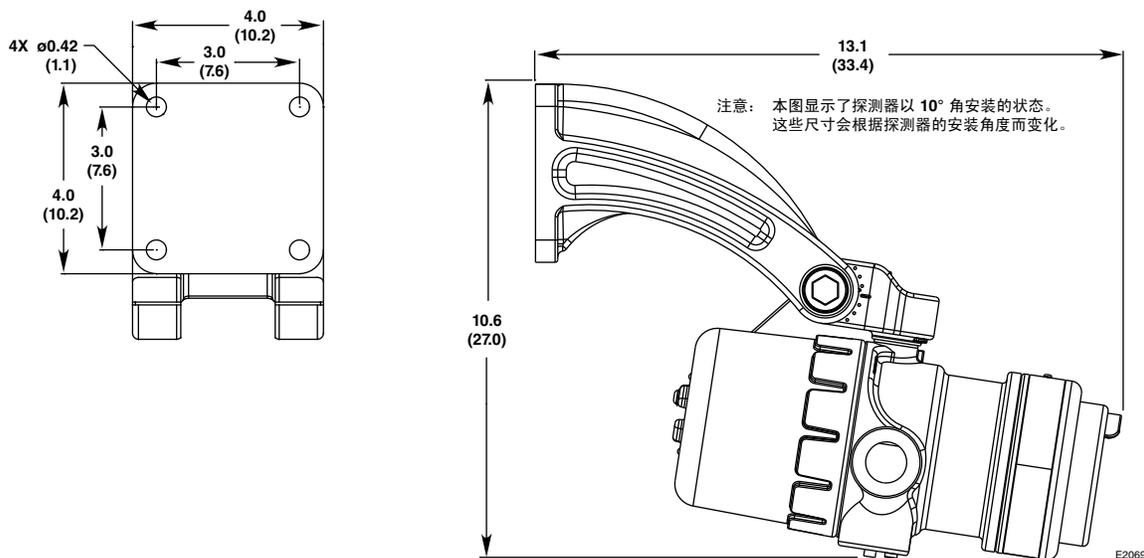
Q9033 安装支架尺寸 (英寸/厘米)
